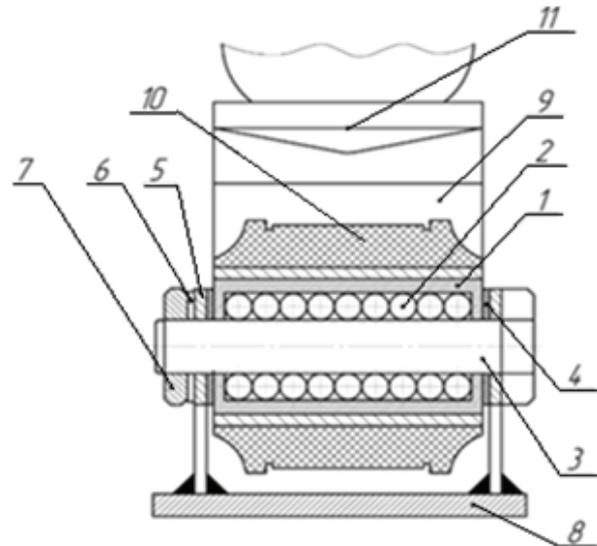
Схема установки РК сайлентблока амортизатора автомобиля
